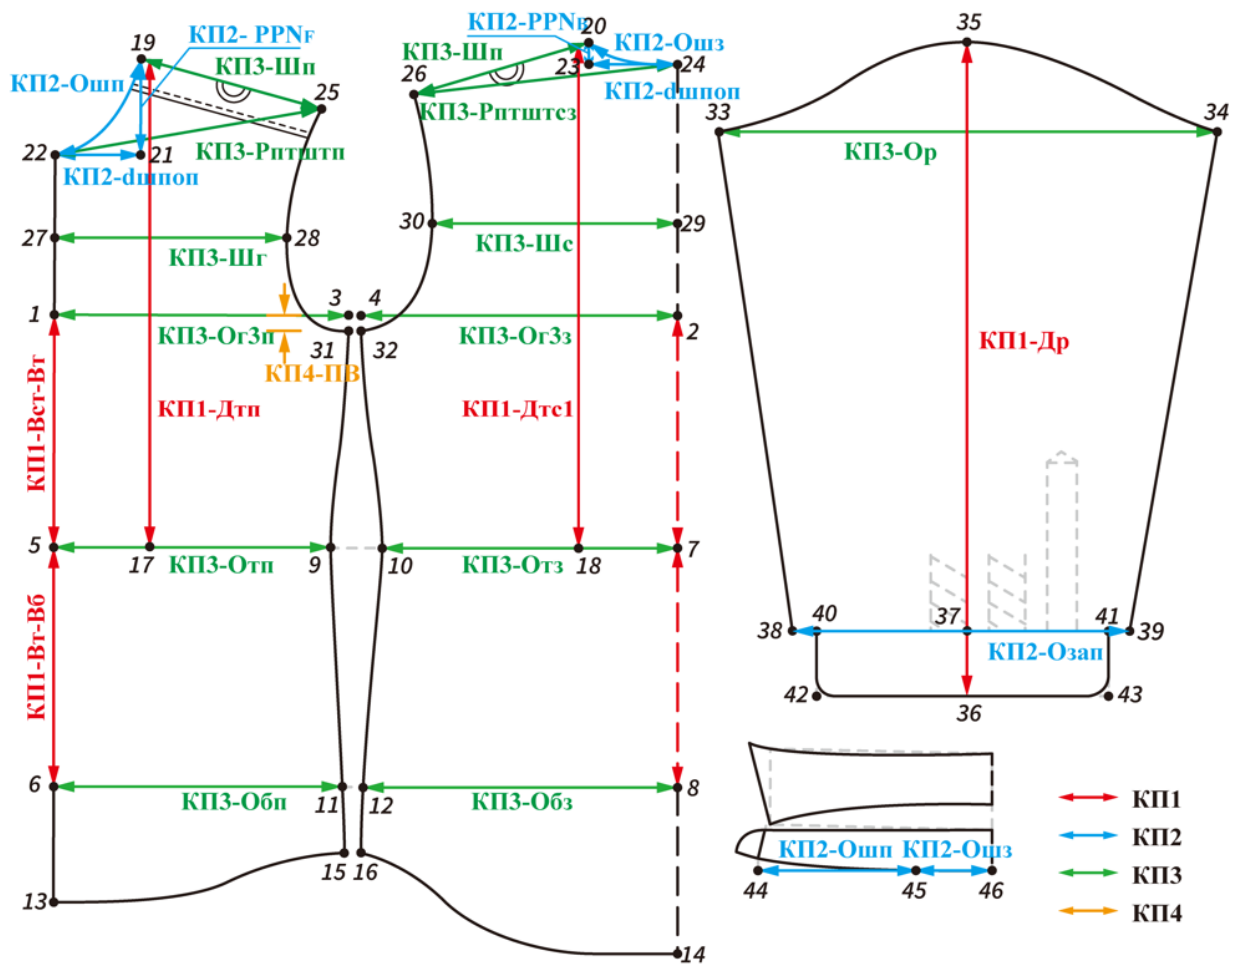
Схема чертежа конструкции мужской сорочки e-bespoke
